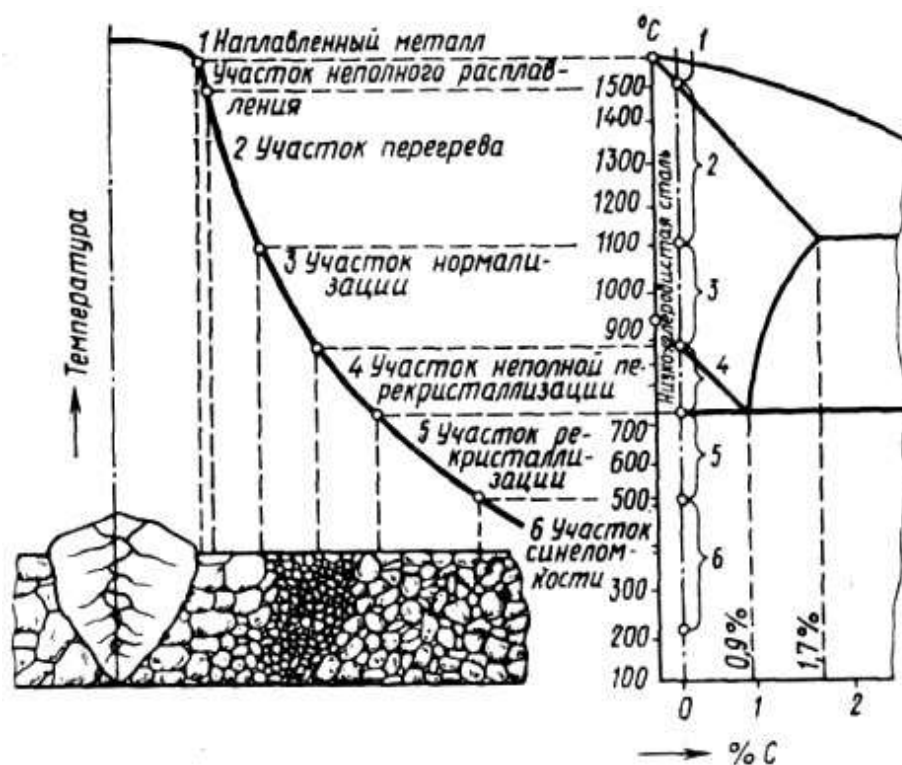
Строение ЗТВ при сварке низкоуглеродистой стали
